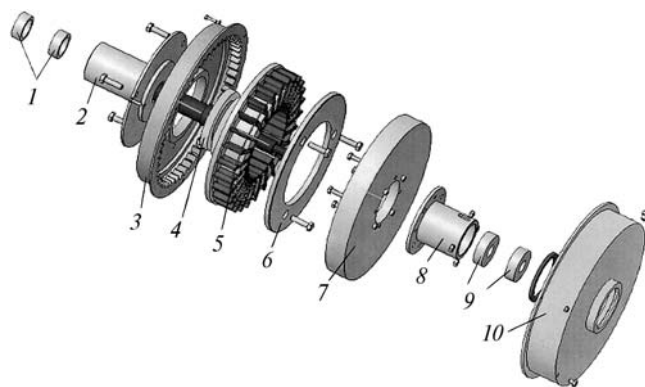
Конструкция плунжерного редуктора ПВР-1
